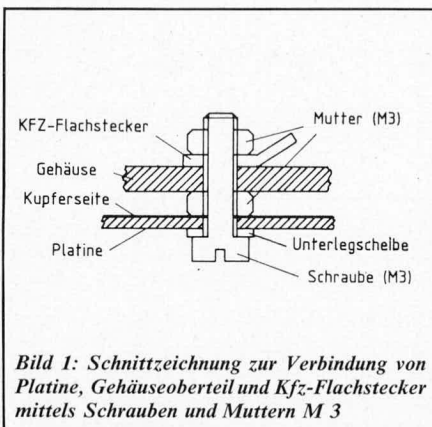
Schnittzeichnung zur Verbindung von Platine, Gehäuseoberteil und Kfz-Flachstecker mittels Schrauben und Muttern M 3
